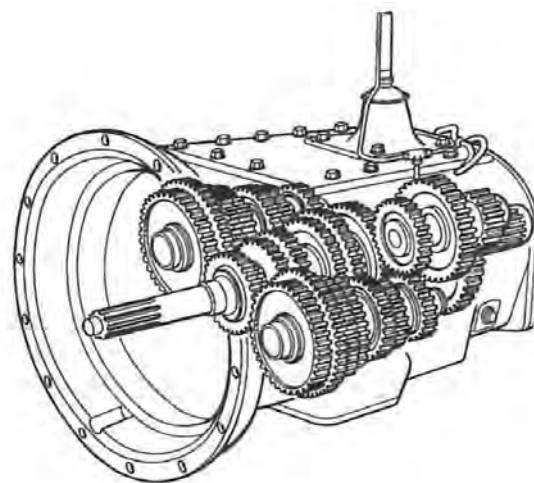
Коробка передач с двумя промежуточными валами фирмы «FULLER»
